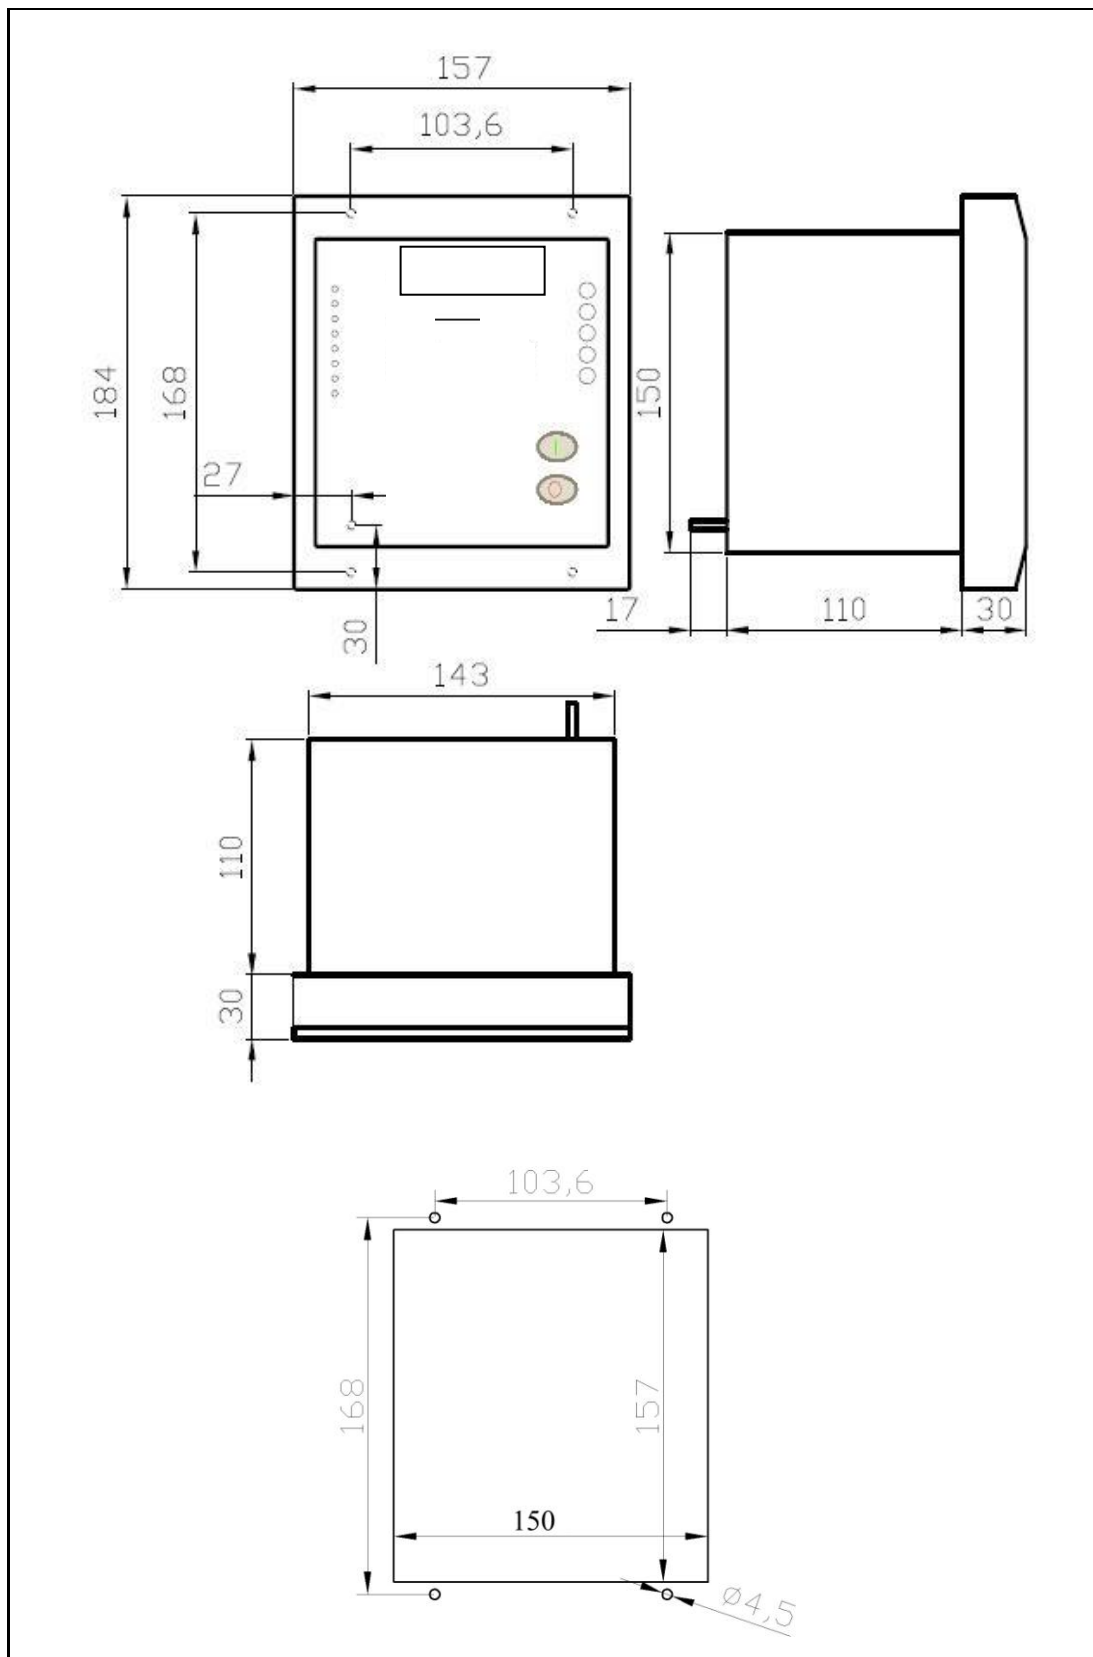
Размеры. Корпус P116 для монтажа "заподлицо"
